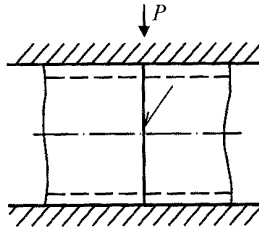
Схема приложения нагрузки при испытаниях образцов с круговым швом
